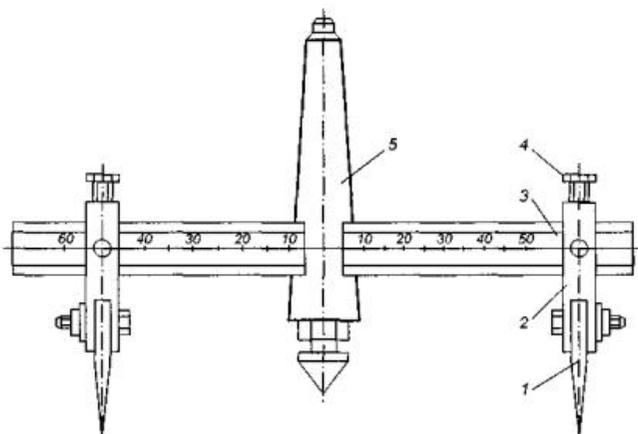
Приспособление для изготовления прокладок для фланцевых соединений:
